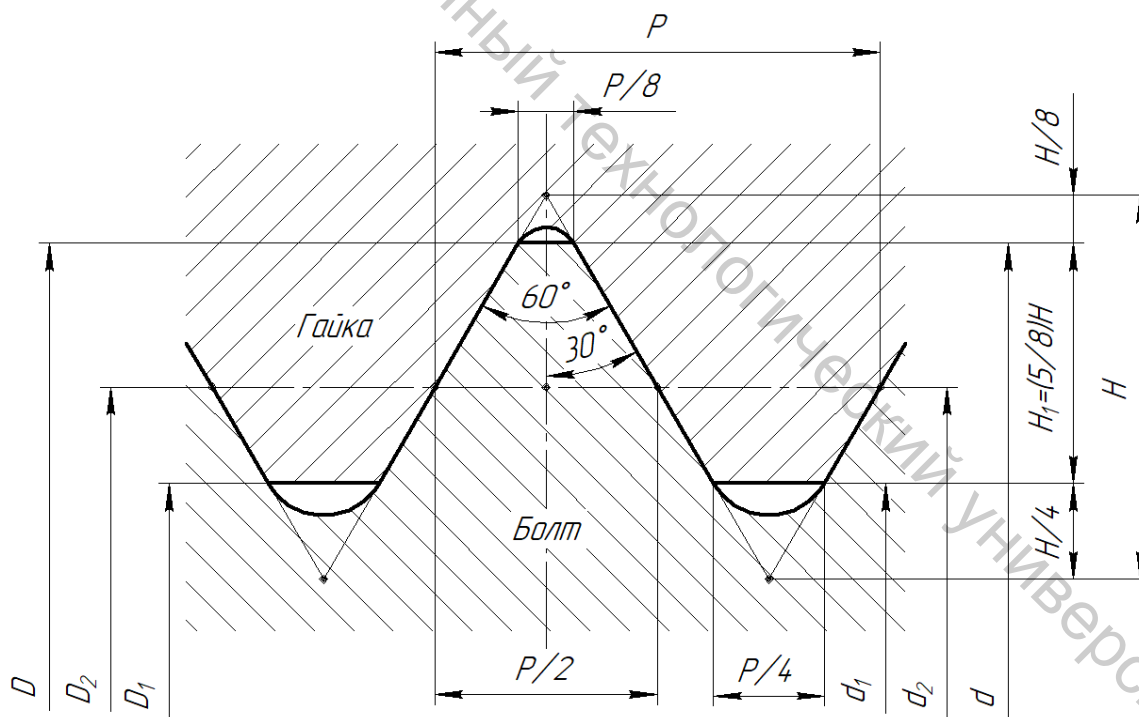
Профиль метрической резьбы и ее основные параметры
